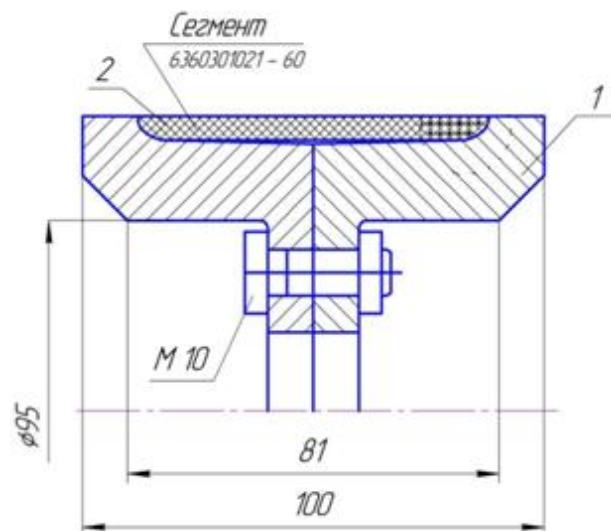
Общий вид модели из стали для получения корковых деталей путём напыления, 1 – модель, 2-напыленное покрытие. / Fig.1. General view of the model of the steel for the cortical parts by spraying 1 - model 2-sprayed coating.
